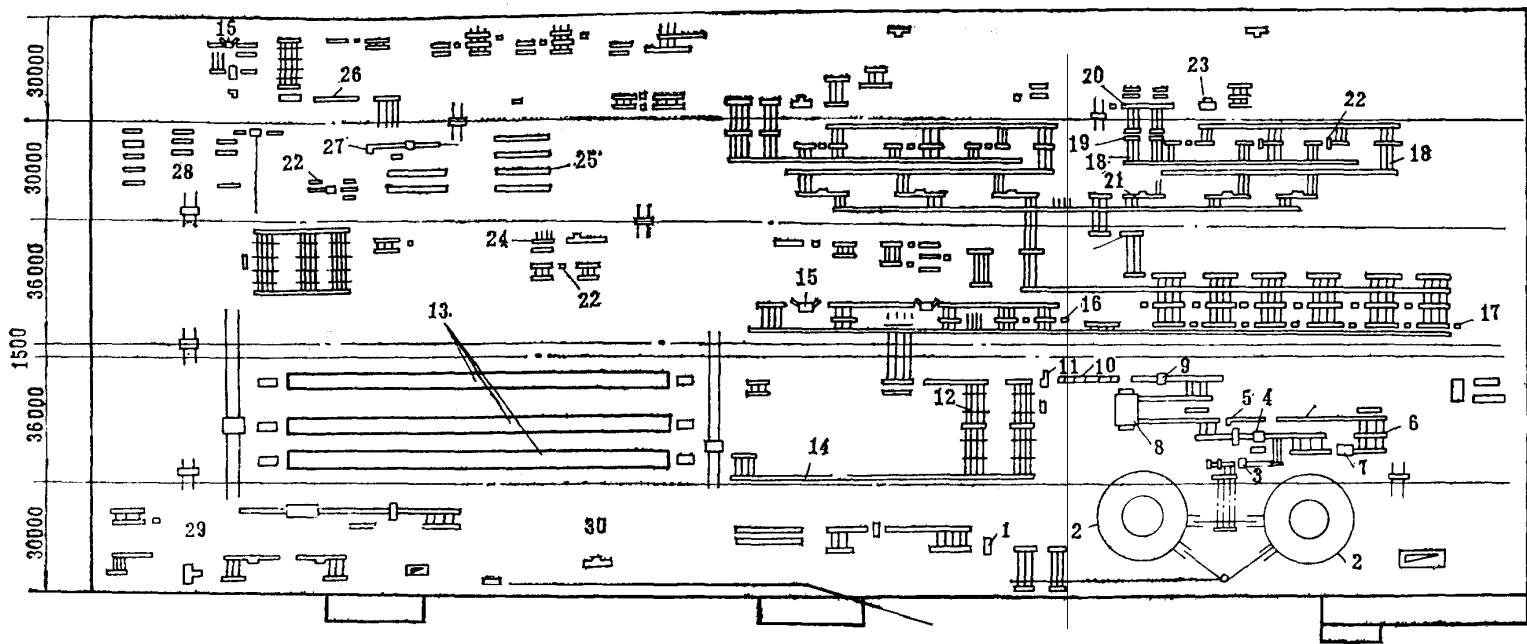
苏联李卜克内西钢管厂三辊轧管机组平面布置图
